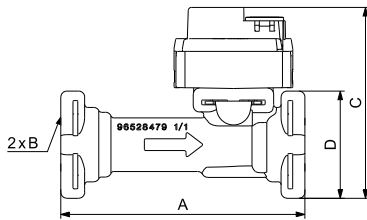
Abmessungen des Sensors MFS 2-20 l/min (ohne Adapter)
